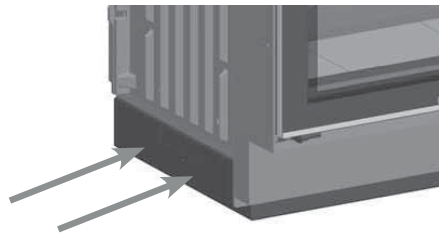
Position der Schrauben für die Paletten-Befestigung
